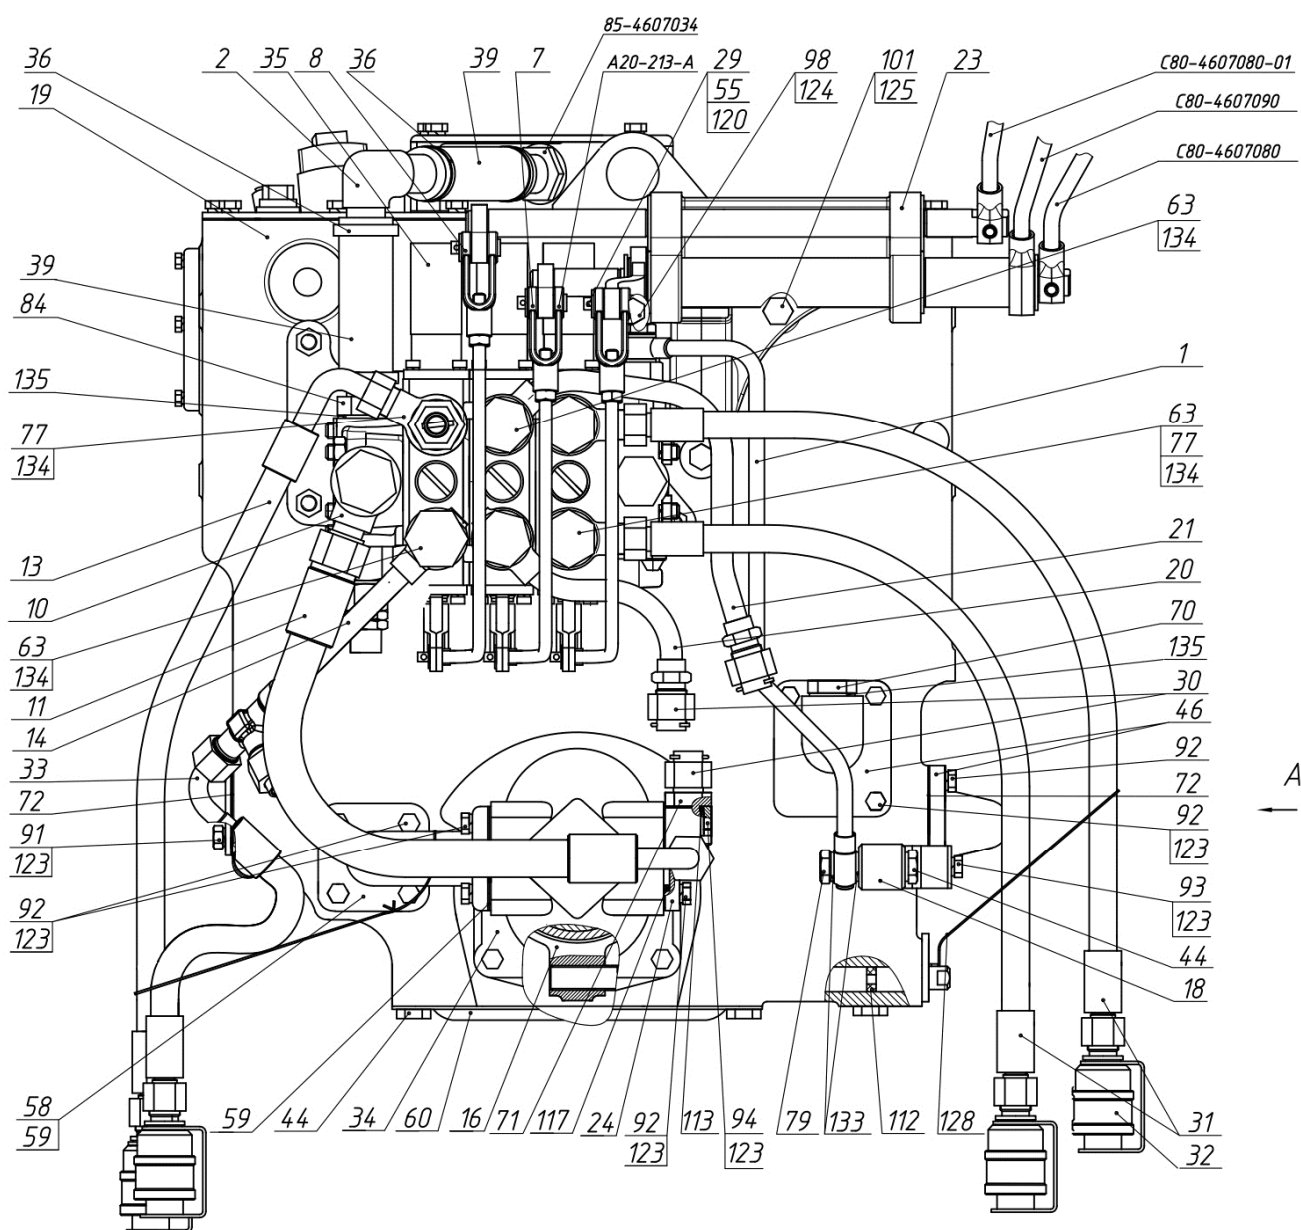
Корпус гидросистемы P85-4600015-01 (лист 1 из 2)
